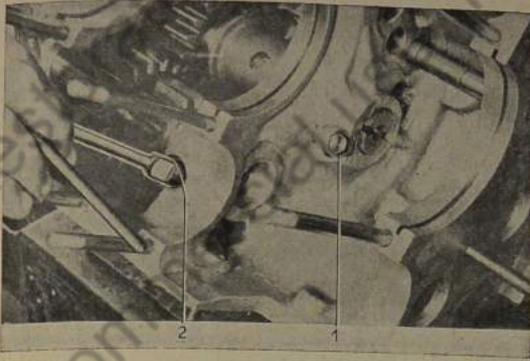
Sicherungsschrauben für Achsen der Schieberäder einschrauben
